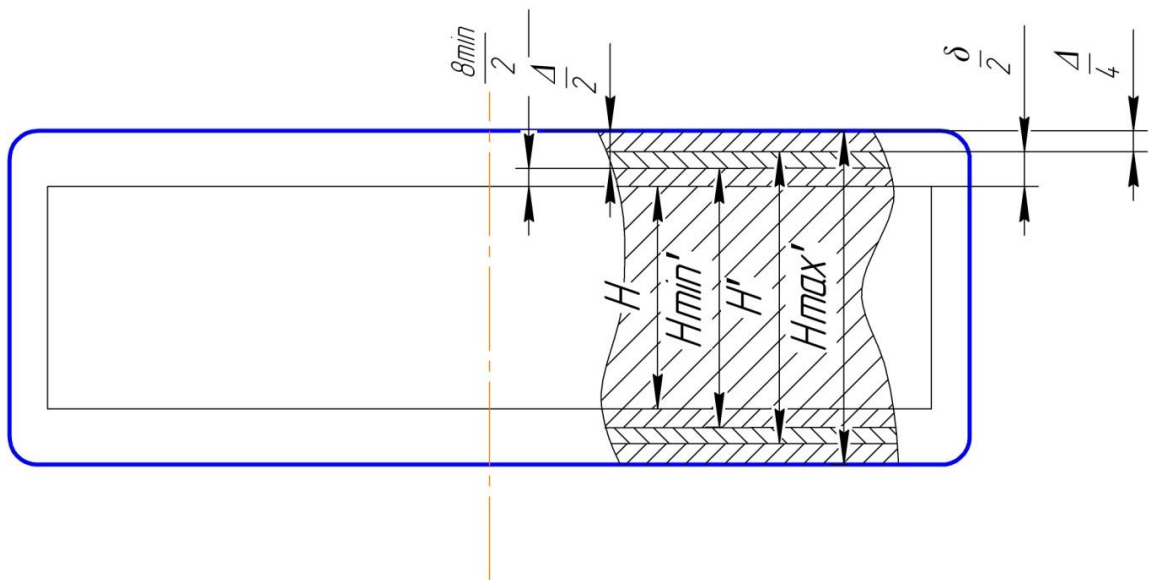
Схема расположения припусков, назначаемых на наружные размеры детали, и предельных отклонений от номинальных размеров поковки: H - обдирочный размер заготовки или номинальный размер детали; δ_{min} - наименьший припуск на размер H ; δ - номинальный припуск на размер H
